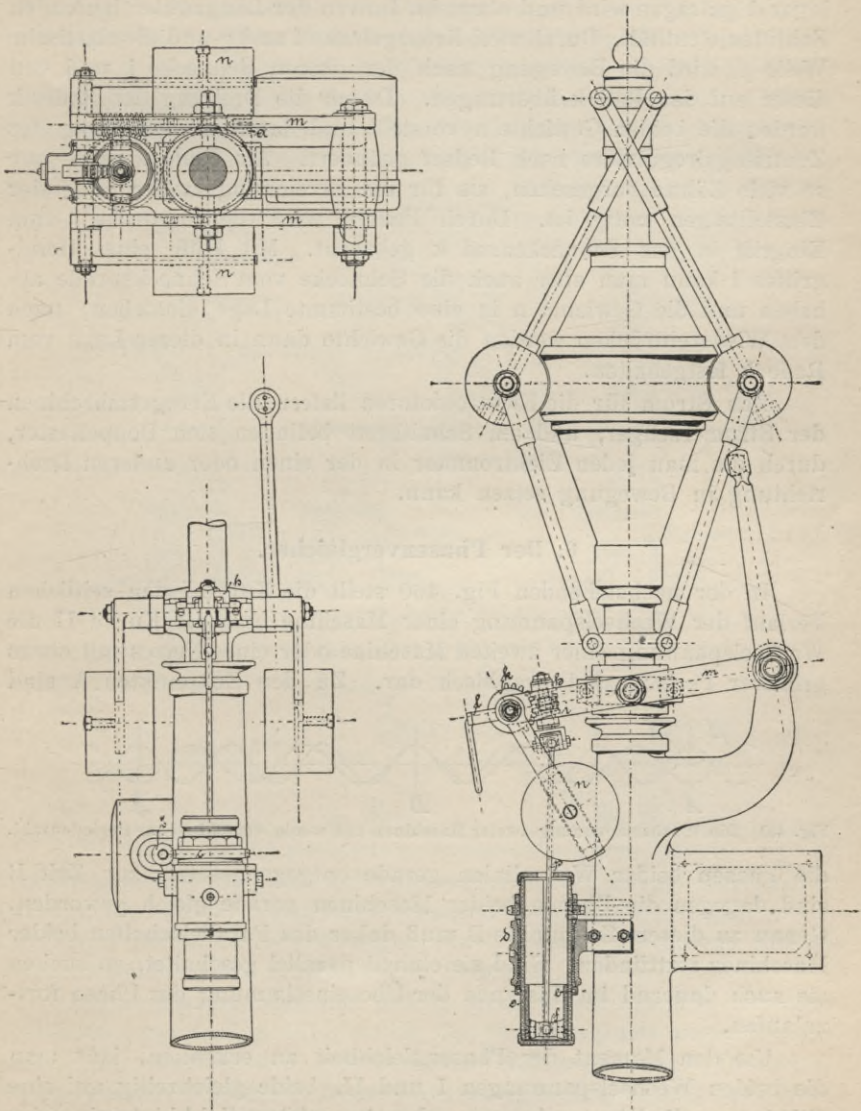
Steuervorrichtung von Siemens & Halske für Dampfmaschinen, die parallel geschaltete Wechselstrommaschinen antreiben.
